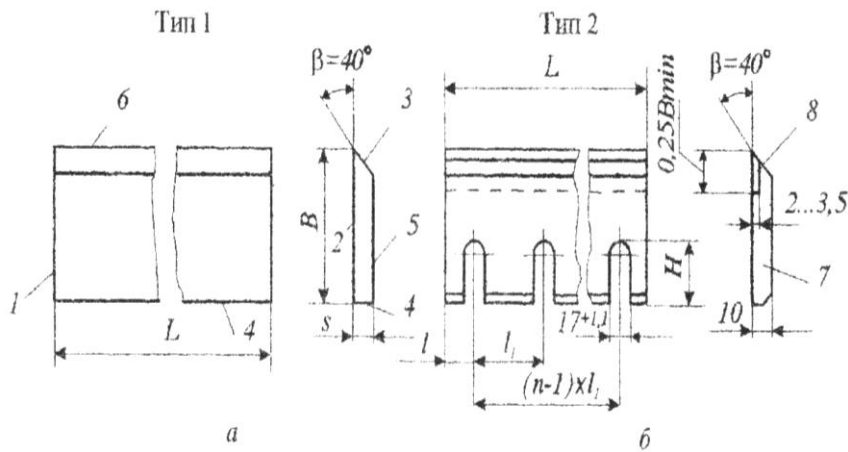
Конструкції тонких ножів для фрезерування деревини: *a* - тип 1 без прорізів; *б* - тип 2 з прорізами; 1 - торцева поверхня; 2 - передня поверхня; 3 - задня поверхня; 4 - поздовжня поверхня; 5 - зовнішня поверхня; 6 - різальна крайка; 7 - корпус ножа; 8 - різальна частина.
